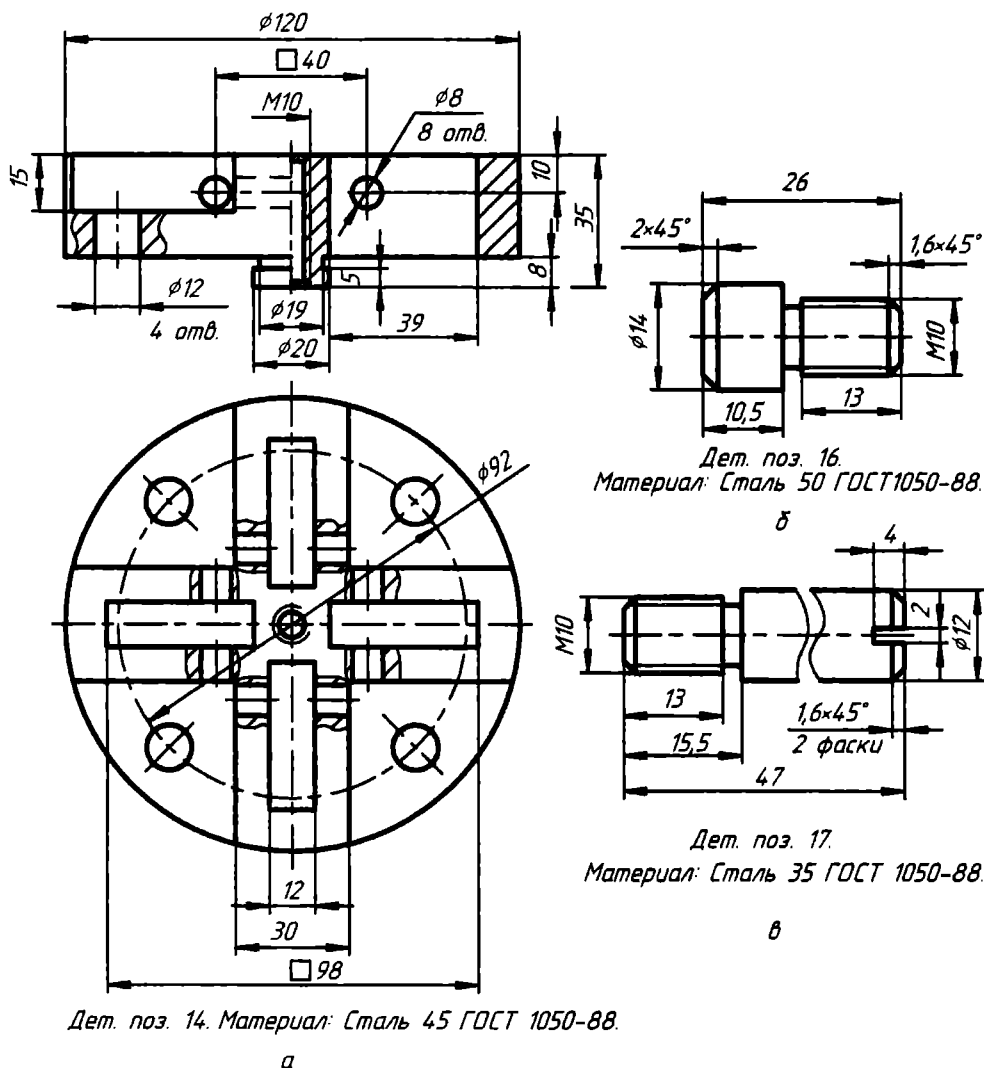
Чертежи: а — крестовины; б — упора; в — пальца
